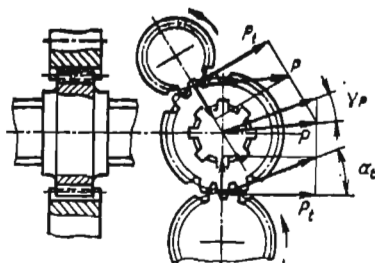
Соединение промежуточного зубчатого колеса с валом (группа РР)
